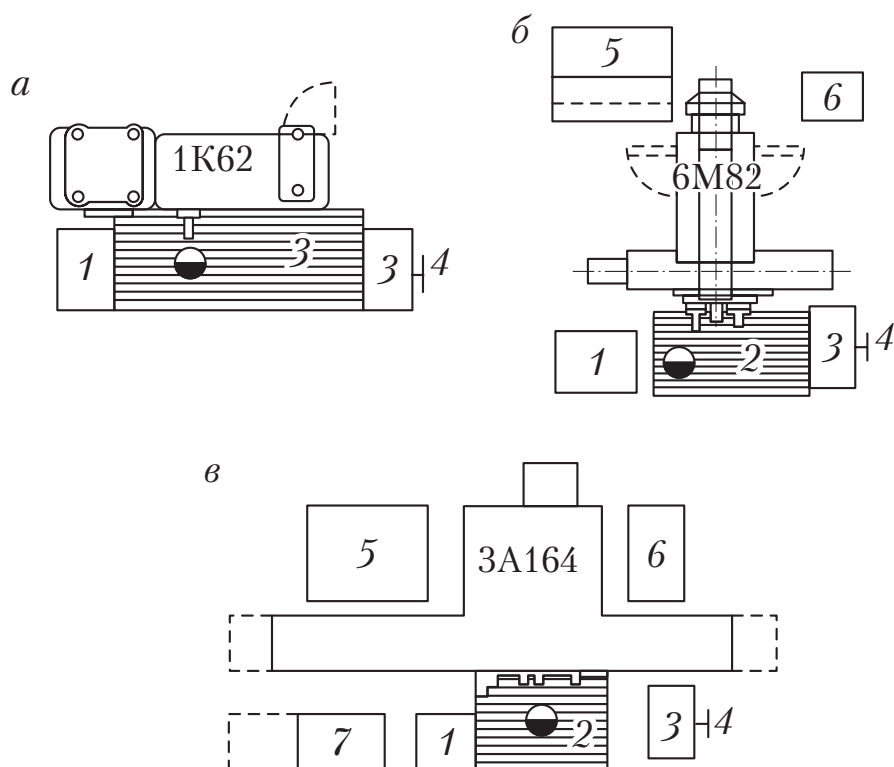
Примеры планировки рабочих мест токаря (а), фрезеровщика (б), шлифовщика (в):
